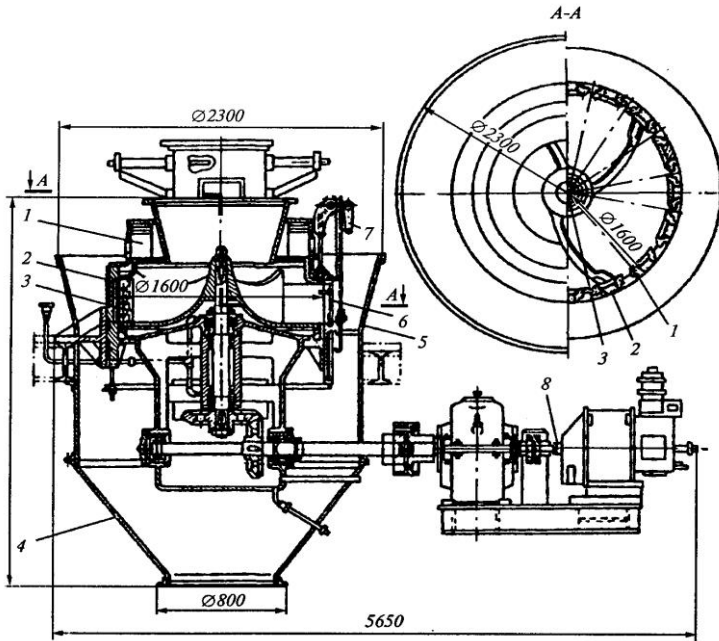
Відцентрова бурякорізка СЦБ – 16М: 1 – бункер; 2 – циліндричний корпус; 3 – трьохлопатевий завиток; 4 – нижній кожух; 5 – верхній кожух; 6 – ножеві рами; 7 – лебідка; 8 – привід
